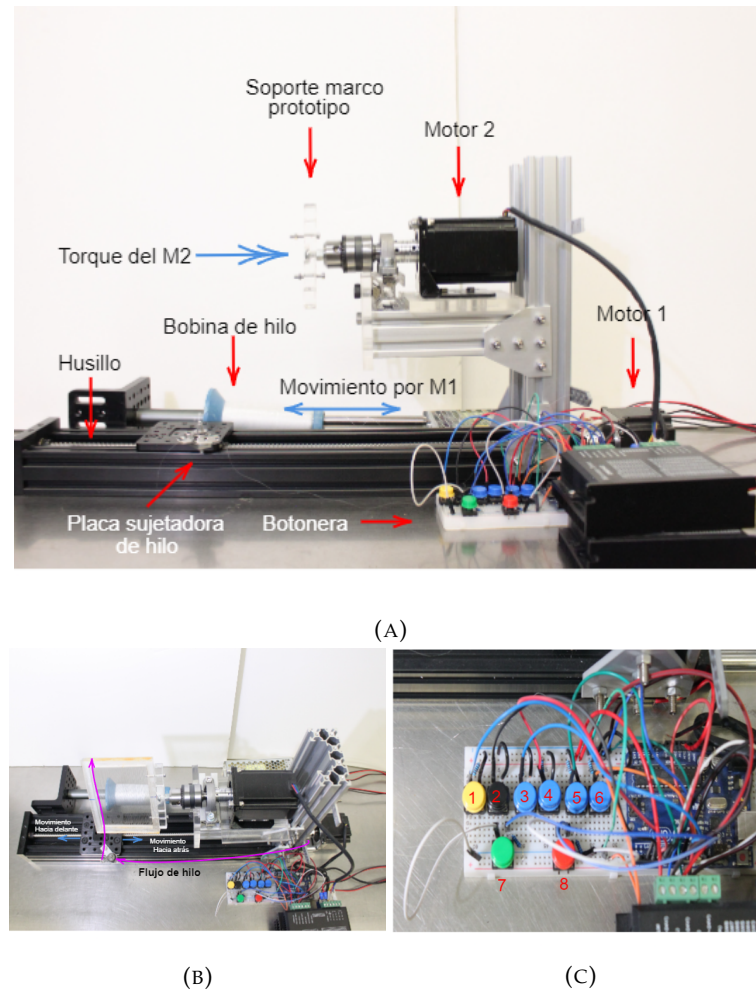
A) Vista frontal máquina de bobinado de hilo y componentes principales. B) Flujo del hilo con el cual se fabrican los prototipos. C) Circuito eléctrico máquina con detalle de botones.
